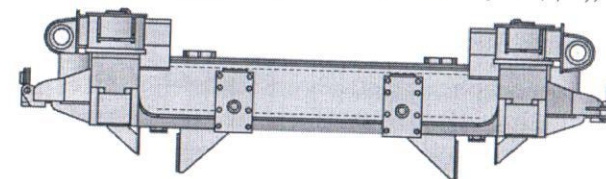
Контроль околошовных зон сварного соединения боковых стенок поперечных балок рамы с верхним и нижним поясом
